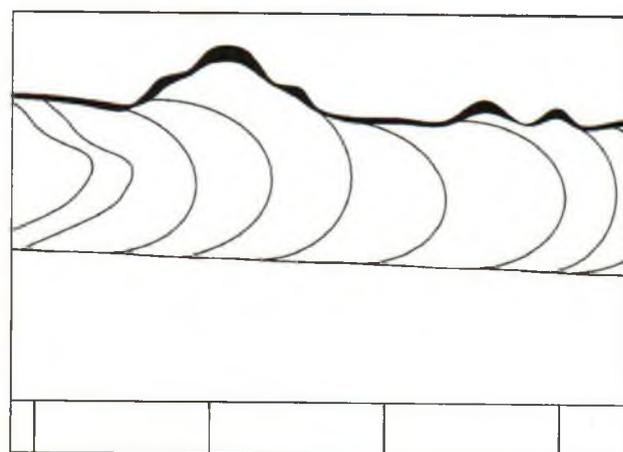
Протяженный подрез в стыковом сварном соединении трубопровода
